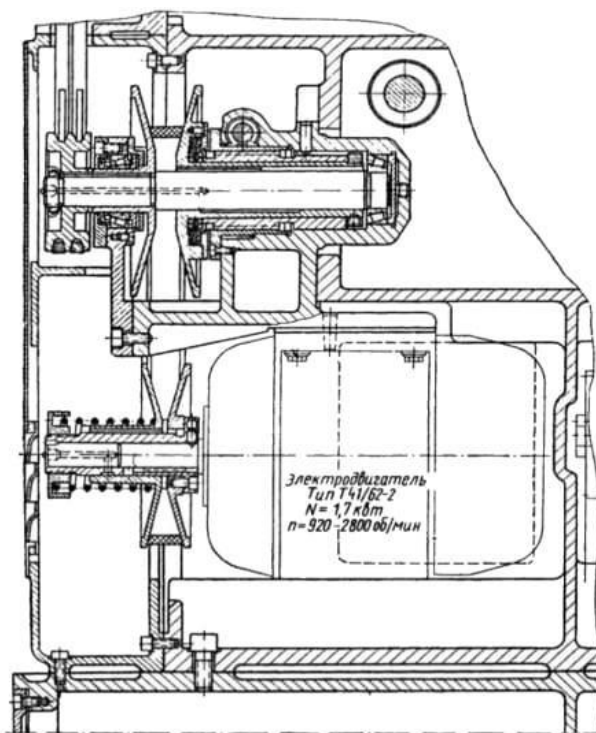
Продольный разрез вариатора, встроенного в привод главного движения зубофрезерного станка 5K301.
